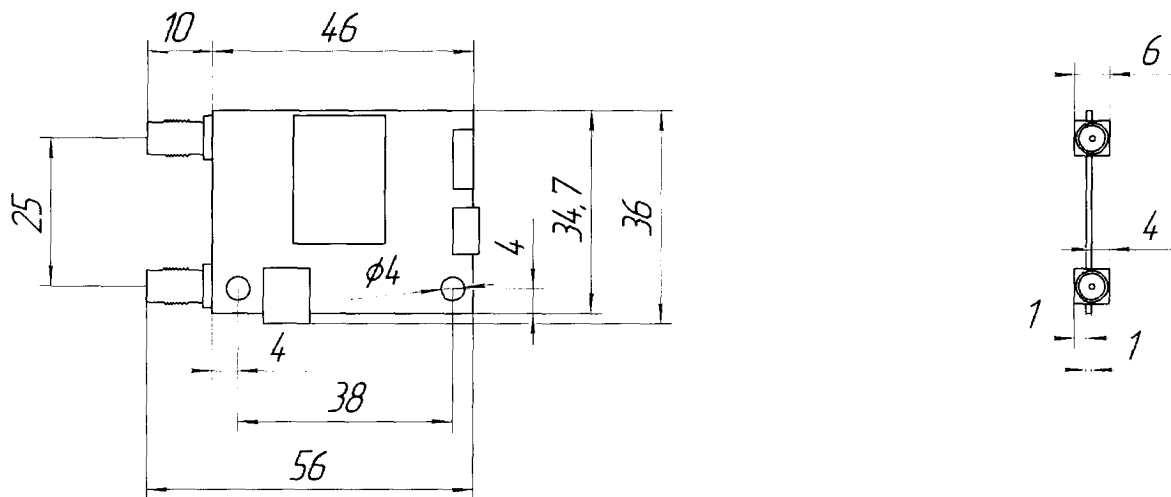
Габаритно-присоединительные размеры изделия MGG2217-01
